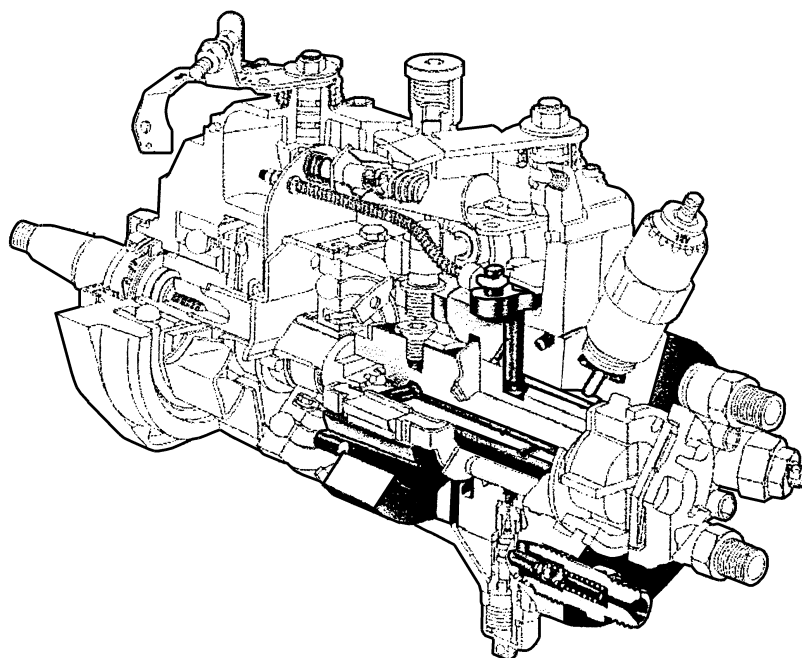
Схема гидравлической головки ТНВД Lucas DPC.
